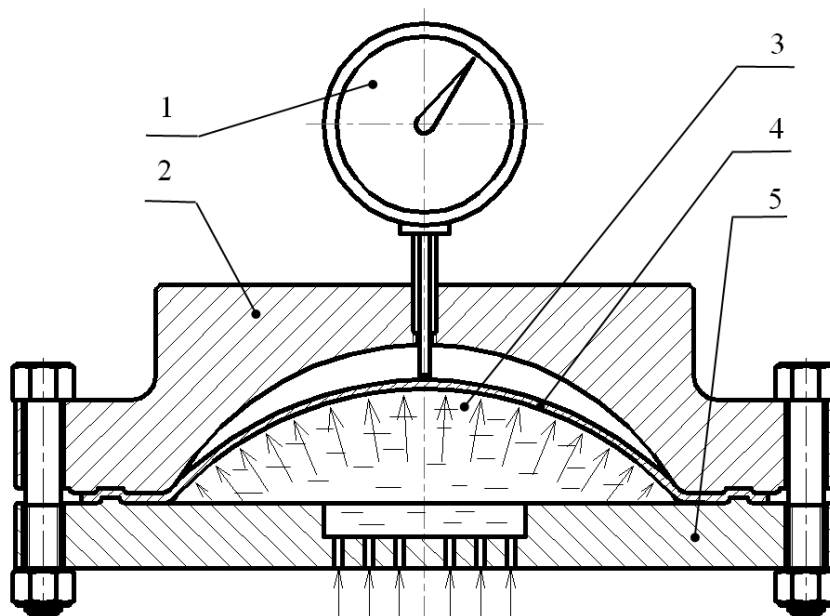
Общая схема проведения формовки-вытяжки и калибровки
